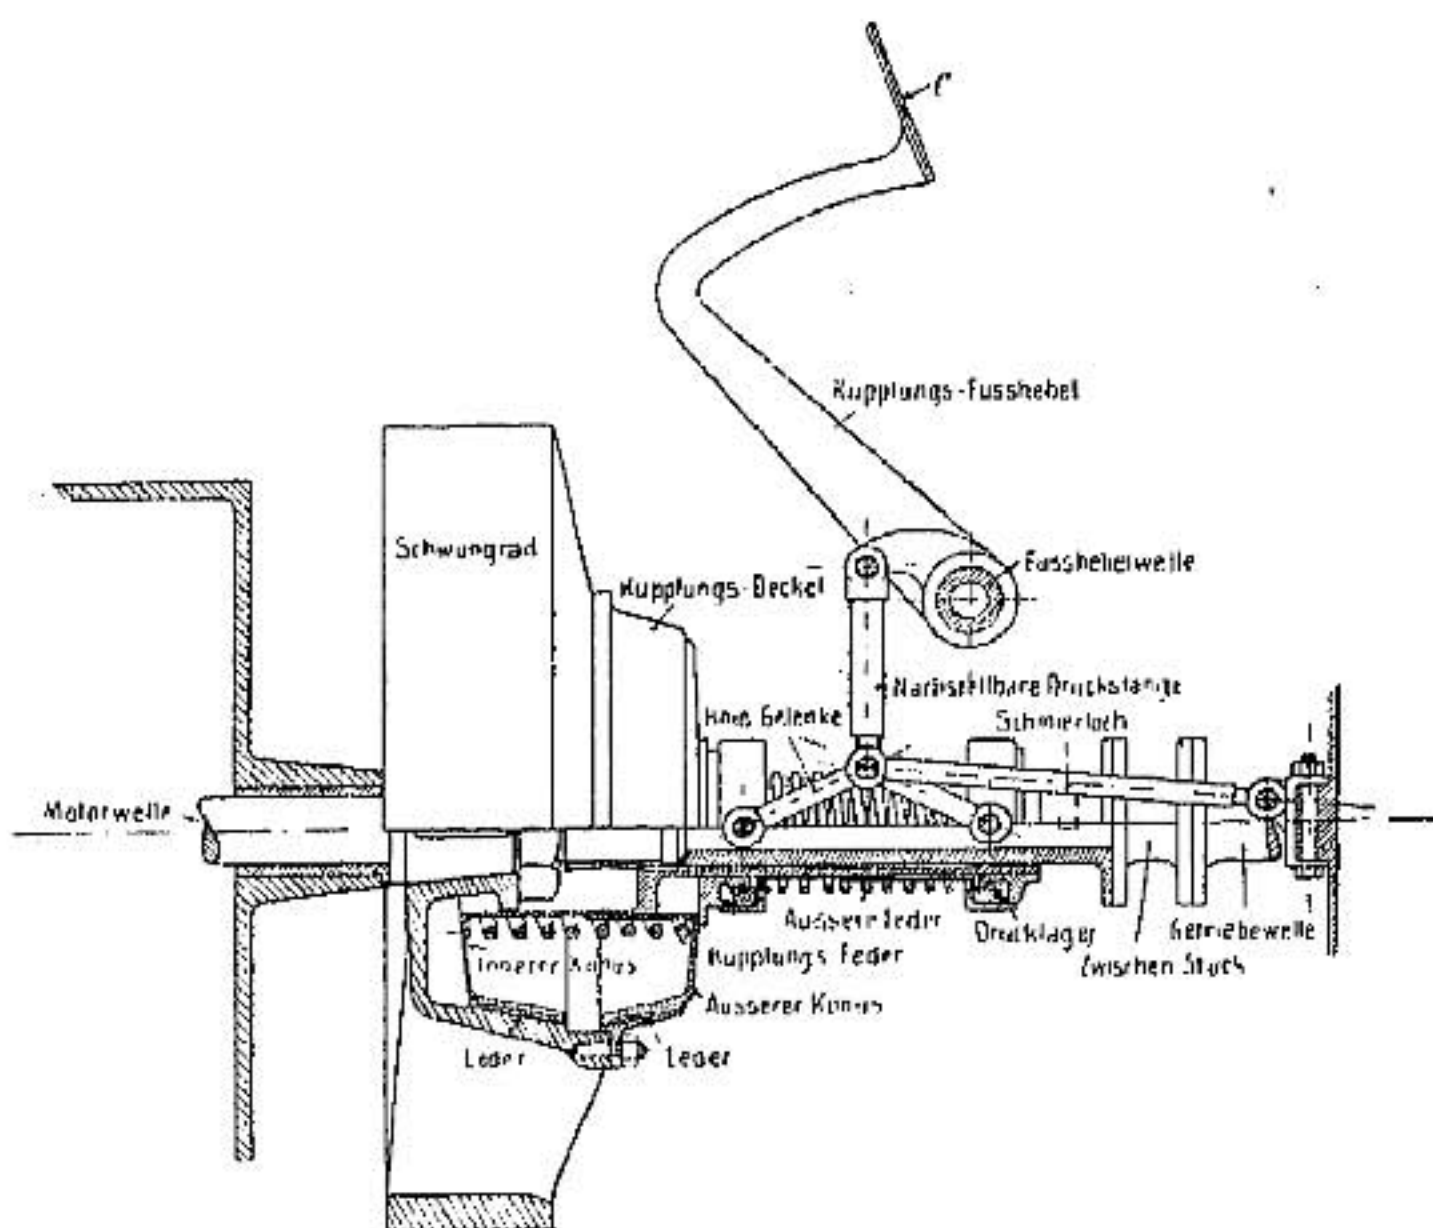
Двойной разгруженный конусъ сцѣпленія шасси Мерседесъ.
